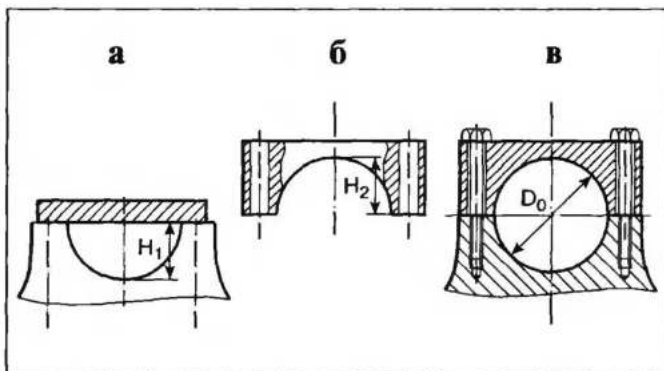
Ремонт опоры с изготовлением новой крышки:
